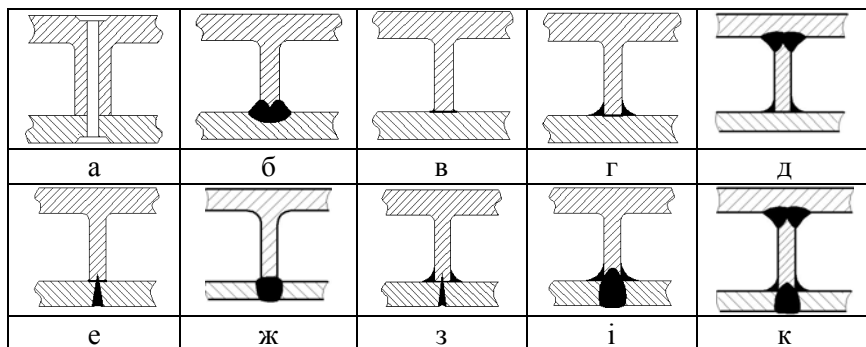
Схема таврового з'єднання лопатки з диском: а – заклепкою; б – кутовими зварними швами; в – високотемпературним капілярним паянням; г – високотемпературним паянням з формуванням великої галтелі; д – приваркою кутовими швами лопатки до основного диска й високотемпературного паяння з формуванням великої галтелі до покривного диска; е – електронно-променевим зварюванням і високотемпературним капілярним паянням; ж – дуговим зварюванням через паз у диску; з – електронно-променевим зварюванням і високотемпературним паянням з формуванням великої галтелі; і – дуговим зварюванням через паз у диска й високотемпературним паянням з формуванням великої галтелі; к – приваркою кутовими швами лопатки до основного диску й високотемпературним паянням з формуванням великої галтелі до покривного диска з електрозаклепками або короткими зварними швами через паз
